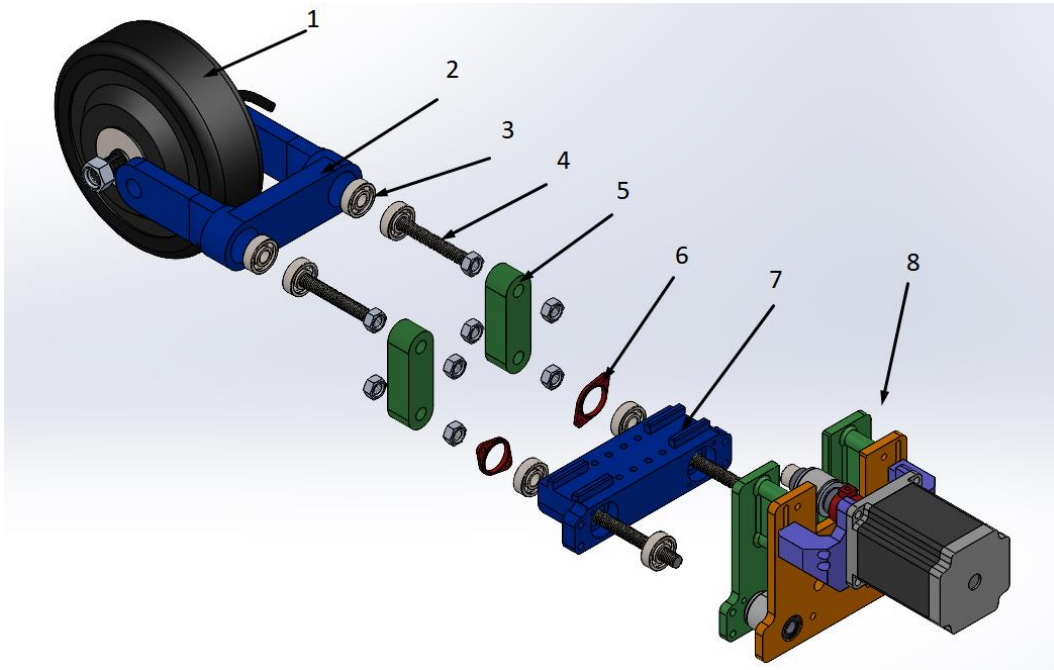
Модель механізму стабілізації положення пристрою: 1) заднє приводне колесо; 2) вилка заднього колеса 3) підшипники серії 608; 4) шпильки M8x60; 5) кривошип; 6) кришки підшипників; 7) корпус; 8) привід механізму
